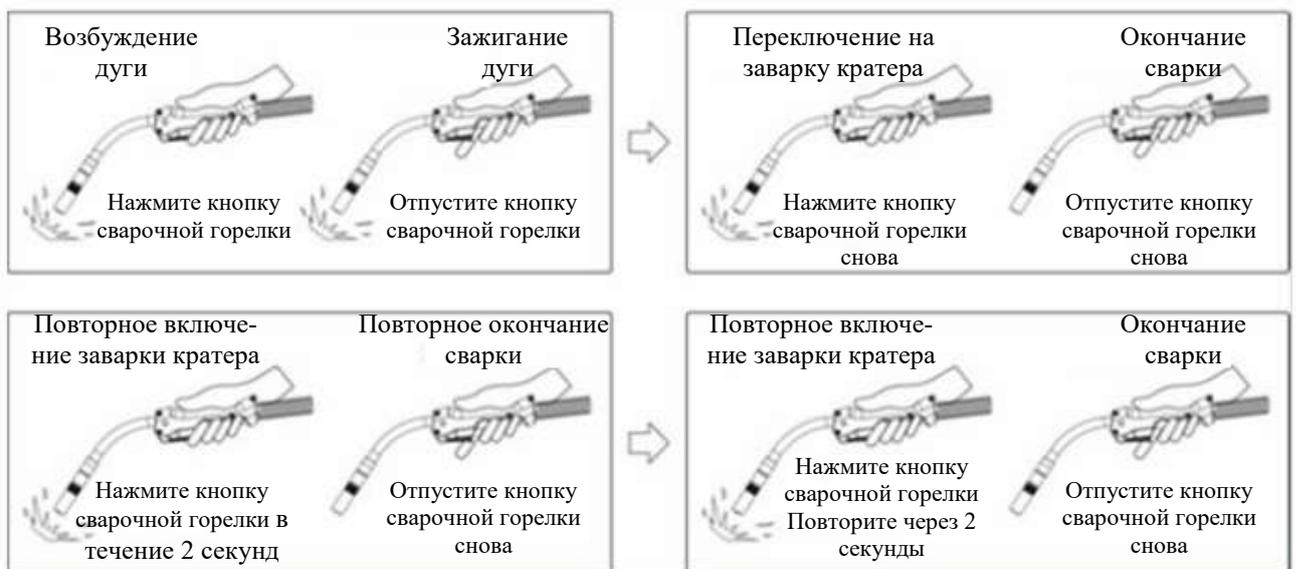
Принципиальная схема сварки с режимом повторной заварки кратера
